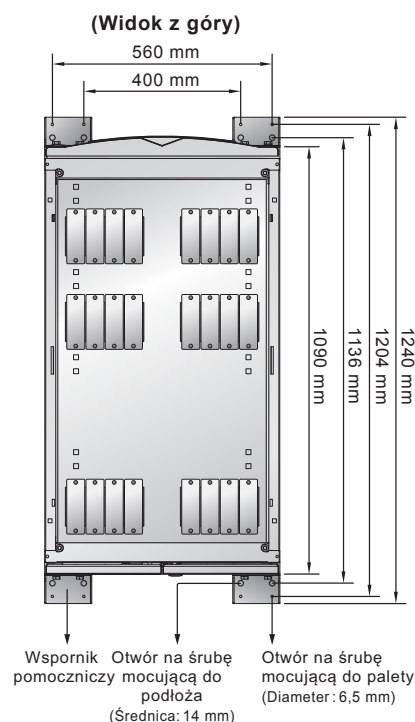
Widok zewnętrzny zasilacza UPS)
